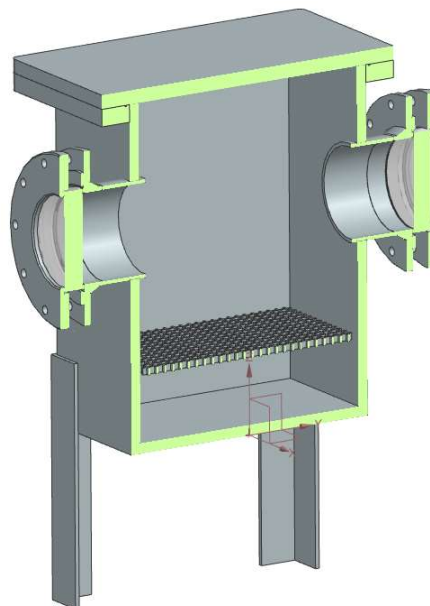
Konzept 3 - CAD-Schnittzeichnung
